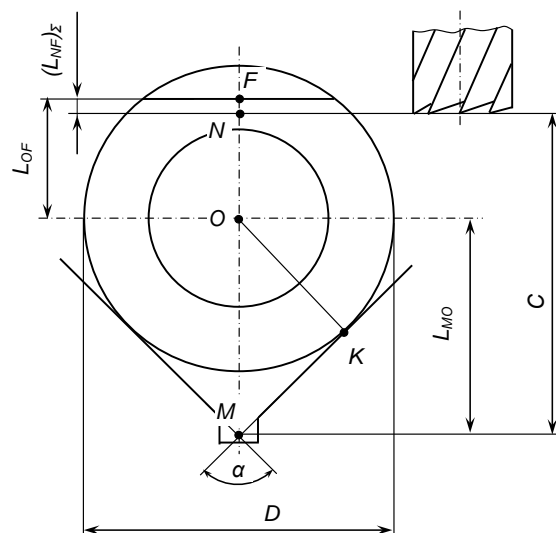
Розрахункова схема з технологічним розмірним ланцюгом для визначення похибки базування як складової мінімального припуску для фрезерування лиски
